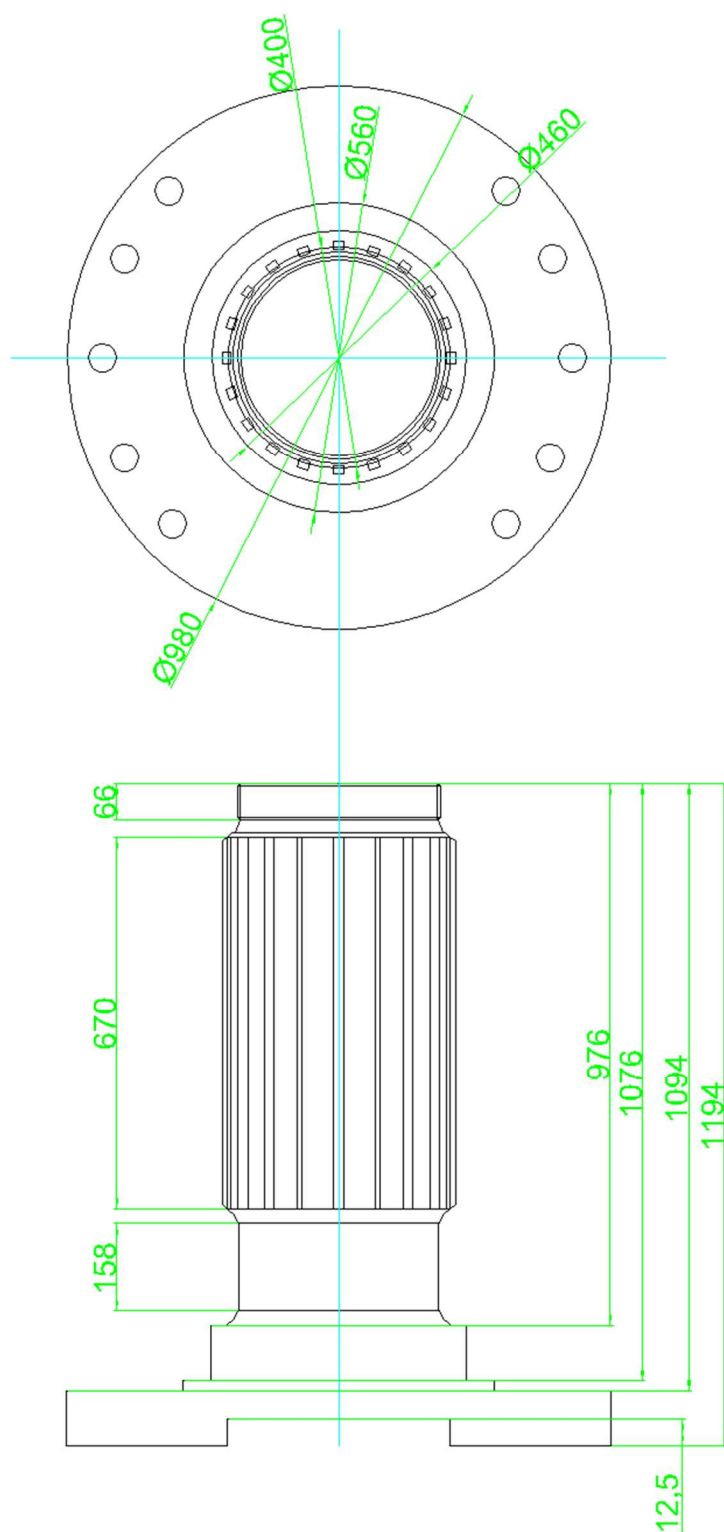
2D креслення деталі шліцевого валу
